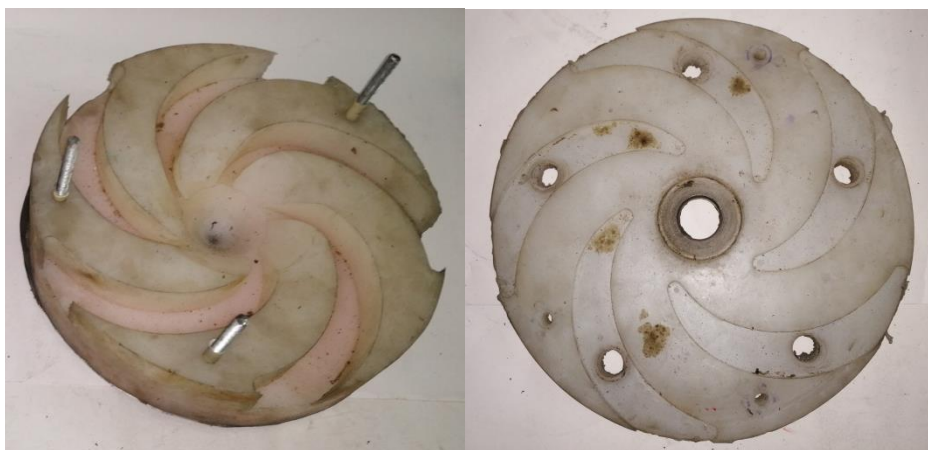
Отливки форм рабочего колеса и литейного силикона
